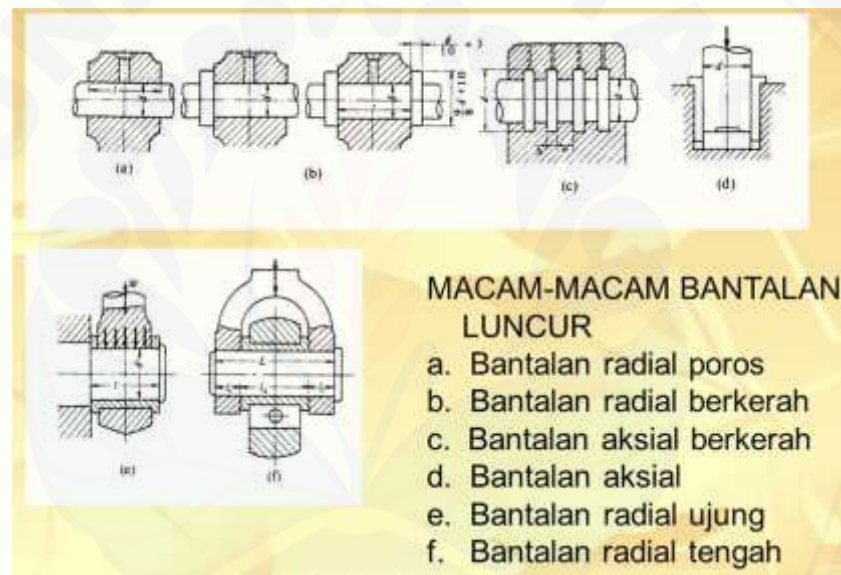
Sliding bearing and rolling bearing* (Hanwha, 2001)
